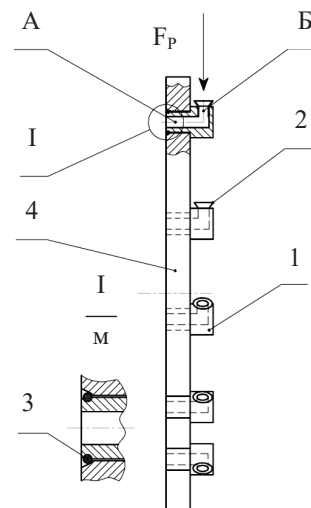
Схема дозуючого диска з поворотними комірками (вид збоку): 1 — поворотна комірка; 2 — сопло поворотної комірки; 3 — стопорне кільце; 4 — висівний диск
